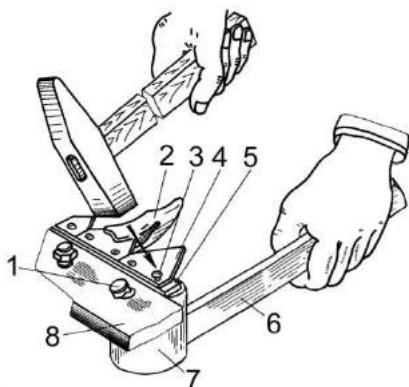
Демонтаж ножа режущего аппарата жатки для трав
